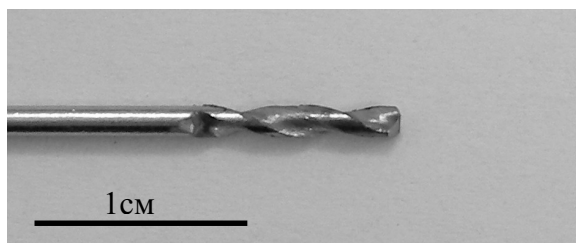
Внешний вид конца спицы, заточенного в форме сверла
